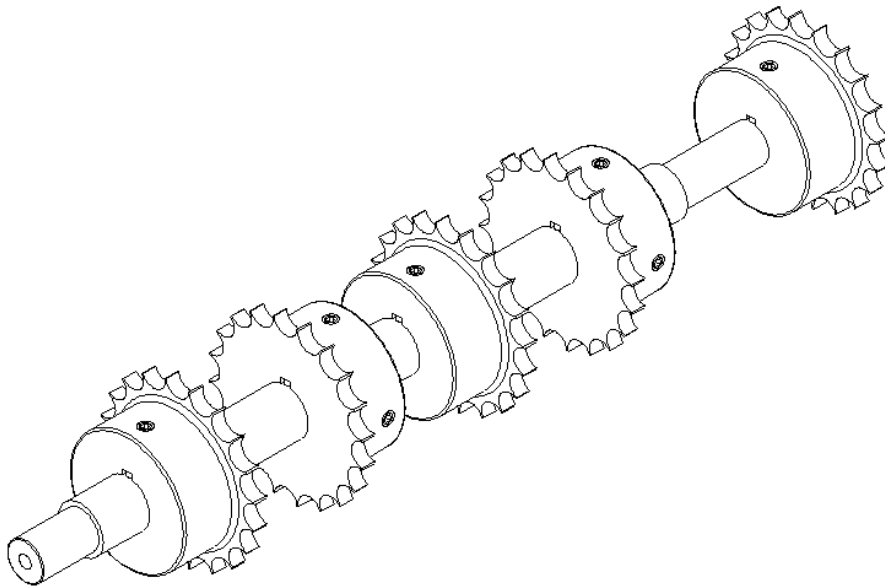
ENSAMBLE ÁRBOL CONDUCTOR
